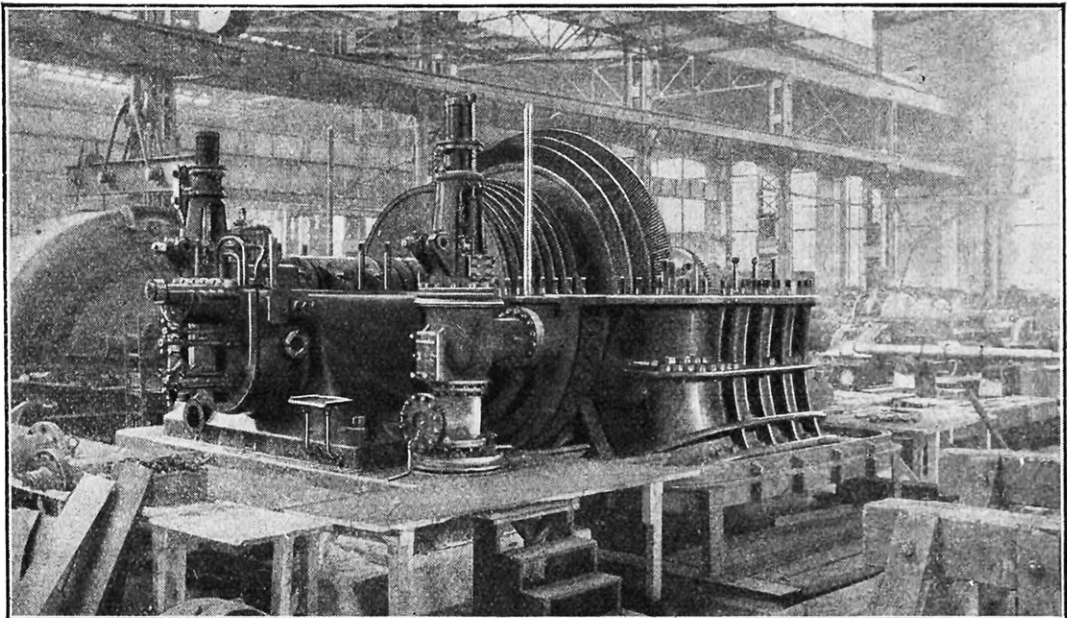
VUE D'UNE TURBINE EN COURS DE MONTAGE, MONTRANT LES 10 ROUES DU ROTOR
